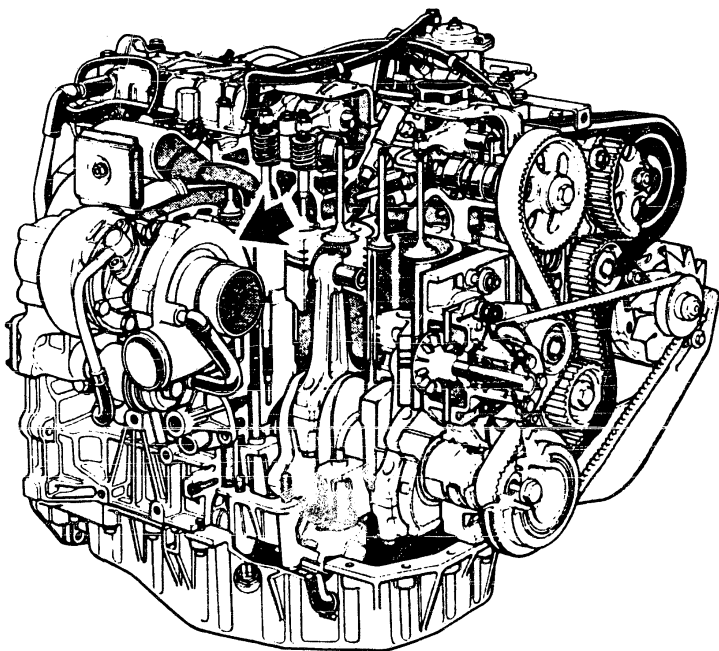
Der Dieselmotor J8S in aufgeladener Ausführung mit dem Turbolader Garrett T3.
